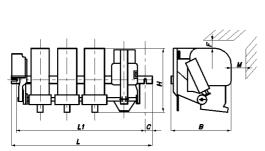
Общий вид и габаритные размеры КТ-5000.
